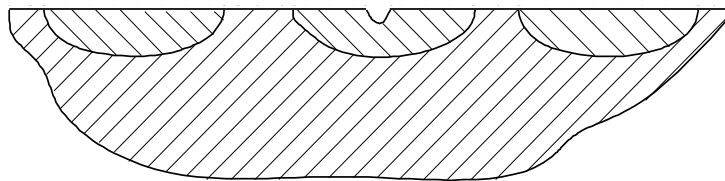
Поверхня після шліфування при неповному видаленні каверн (схема)
